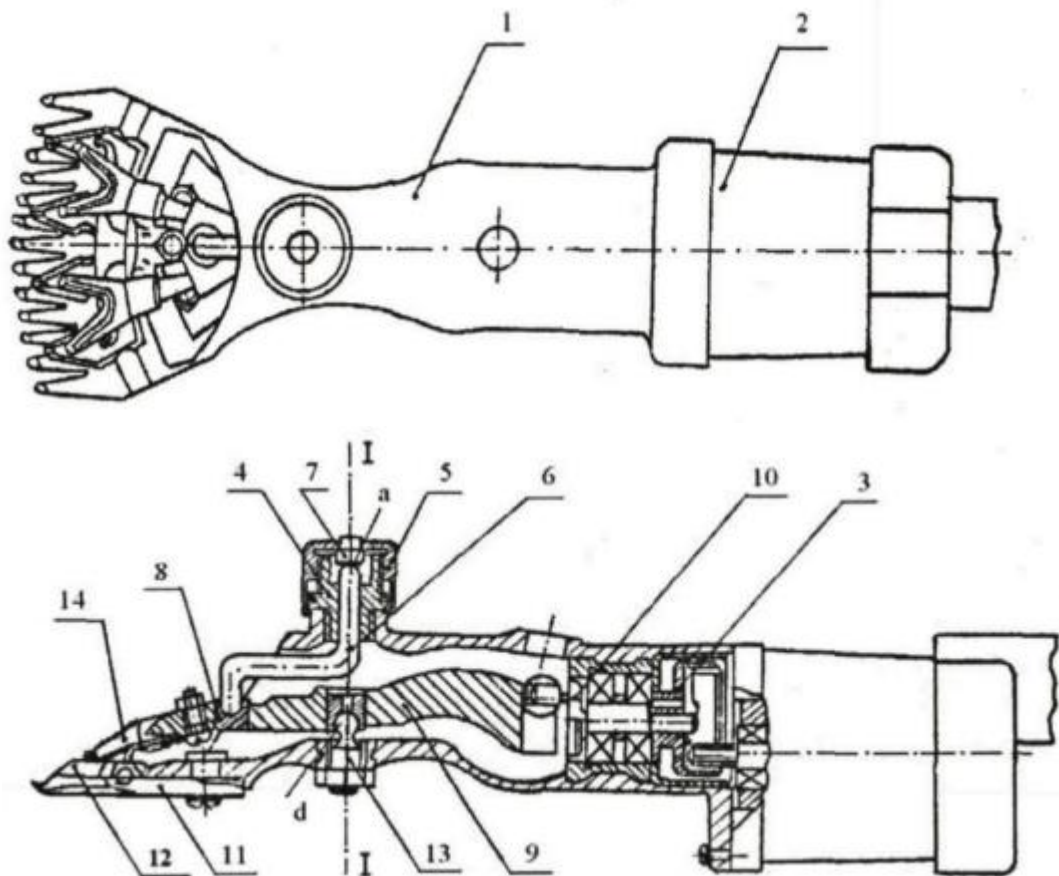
Загальний вигляд машинки з колінчастим натискним стрижнем: 1 - корпус; 2 - електродвигун; 3 - редуктор; 4 - штуцер; 5 - натискна гайка; 6 - колінчастий напологливий стрижень; 7 - упор; 8 - підп'ятник; 9 - важіль; 10 - вал-ексцентрик; 11 - гребінка; 12 - ніж; 13 - центр обертання; 14 - натискні лапки
